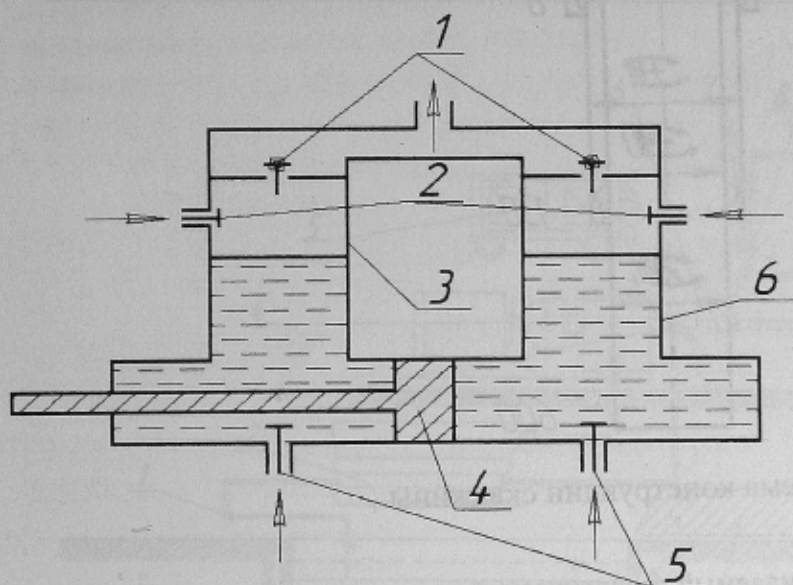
Схема КДУ на базе насоса BWZ—1100/50: 1 — нагнетательный клапан; 2 — клапан для впуска воздуха; 3 — цилиндр; 4 — поршень; 5 — клапан для впуска жидкости; 6 — корпус насоса
